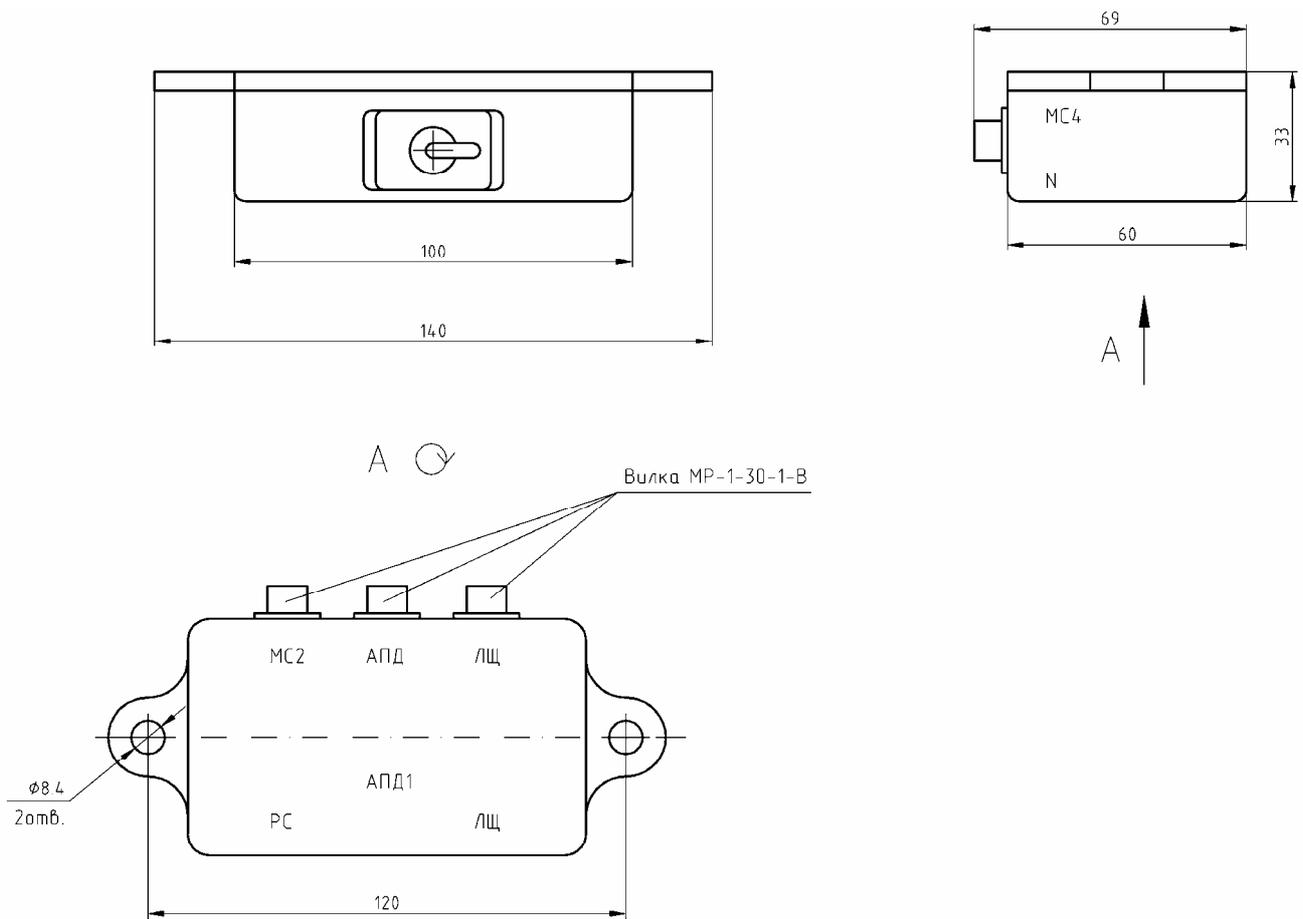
Габаритные чертежи блока сопряжения МС4
